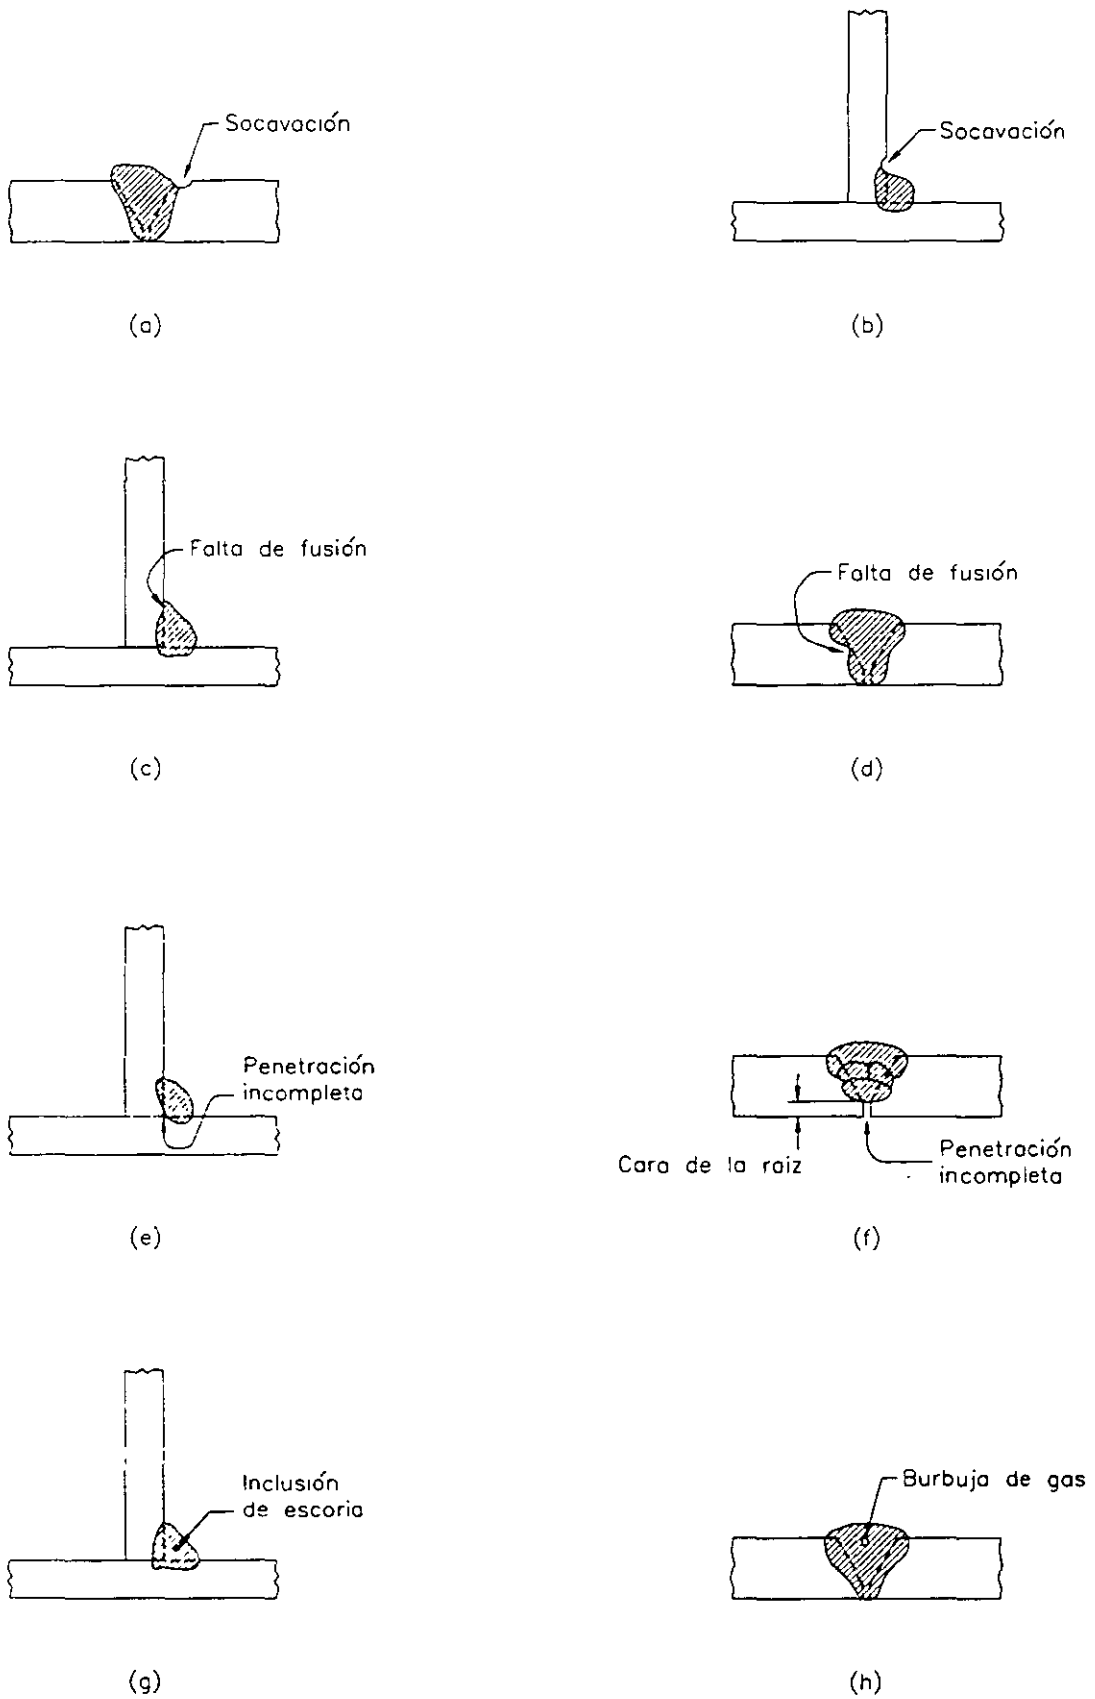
DEFECTOS DE SOLDADURAS
